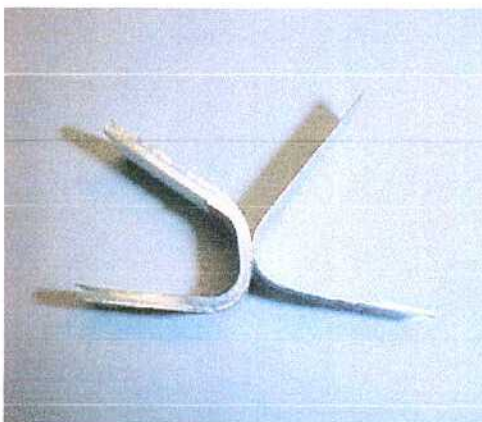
Soldadura Al-SS. Ensayo de despegue.
